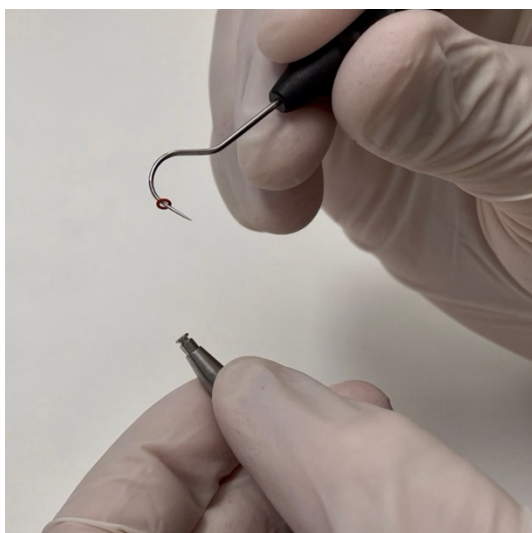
Aufnehmen des O-Rings mit einer Sonde
